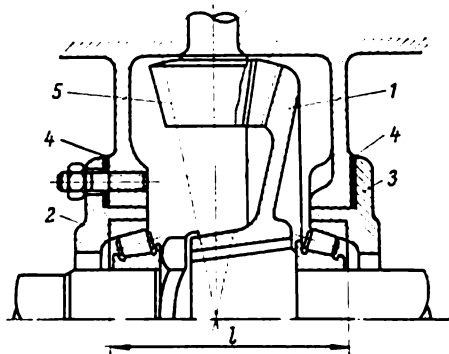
Réglage du jeu d'un engrenage conique à rouleaux coniques
